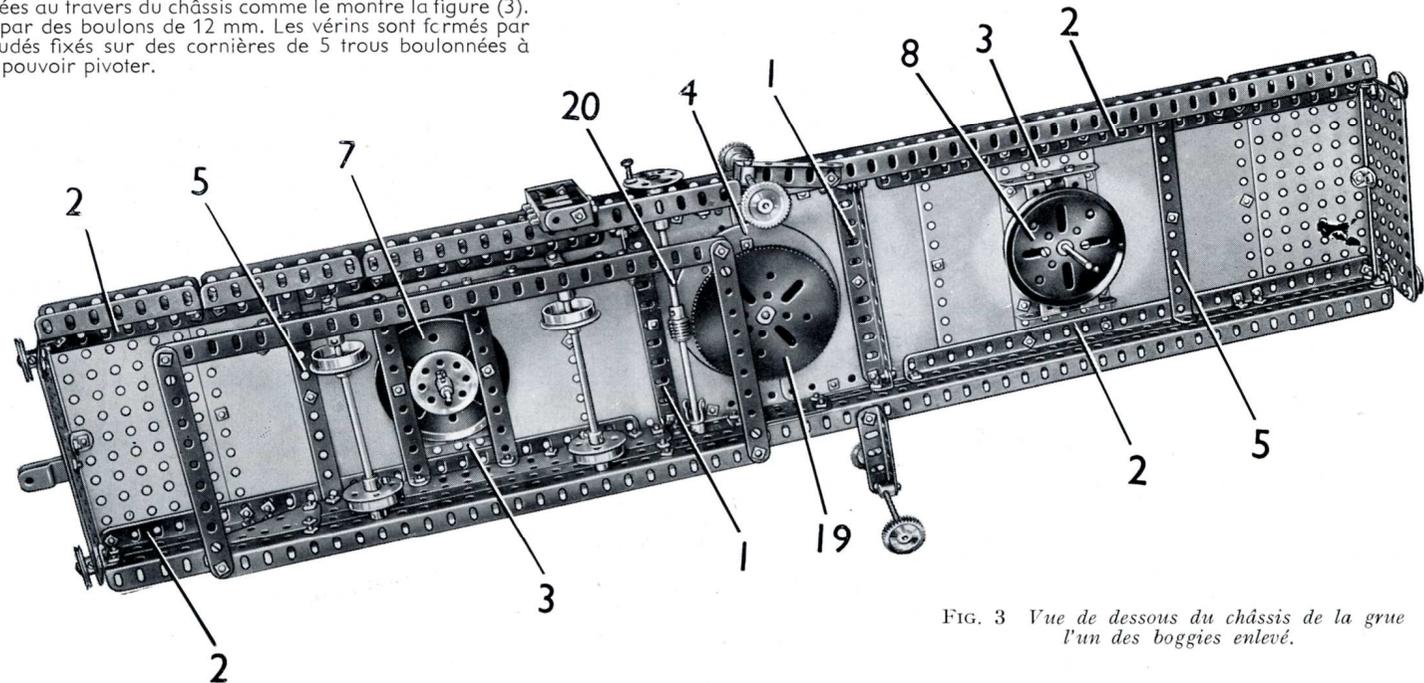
Vue de dessous du châssis de la grue l'un des boggies enlevé.
